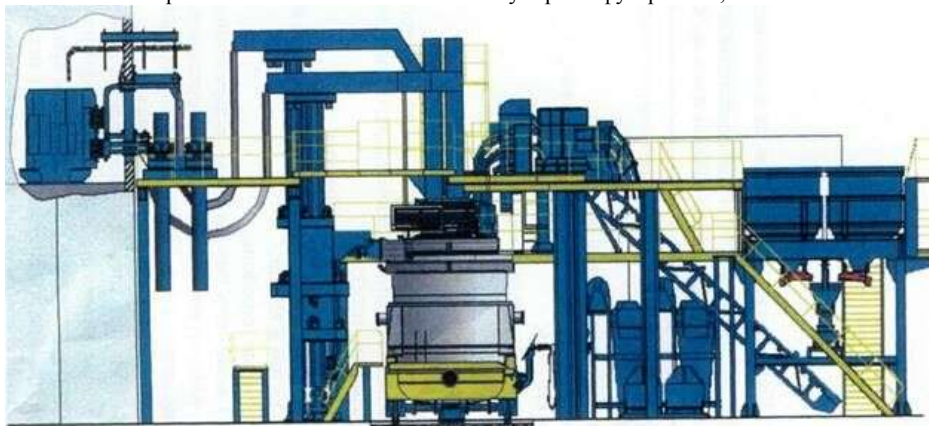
Расположение оборудования агрегата ковш-печь вдоль пролета цеха
